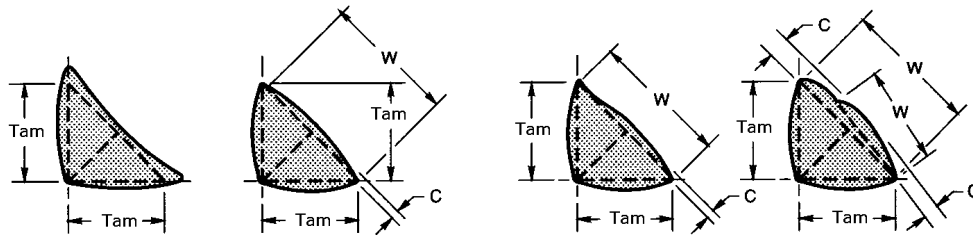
Uso de calibrador de soldaduras
